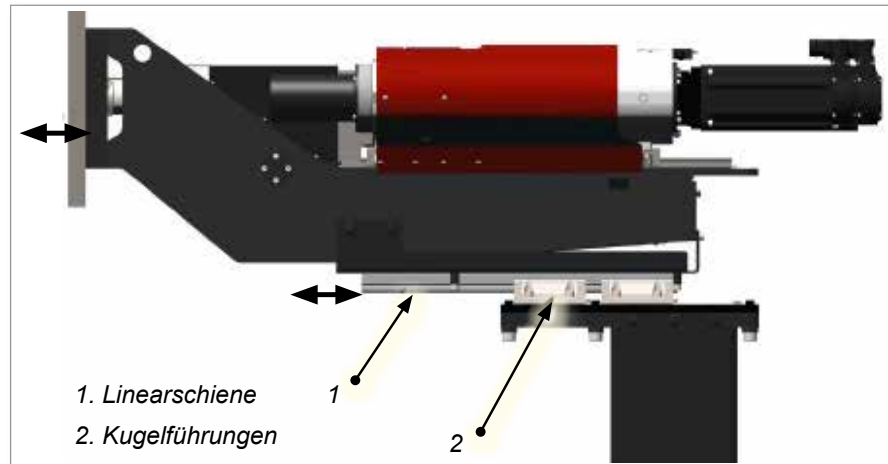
Hochleistungsständer – Einstellung der horizontalen Position
